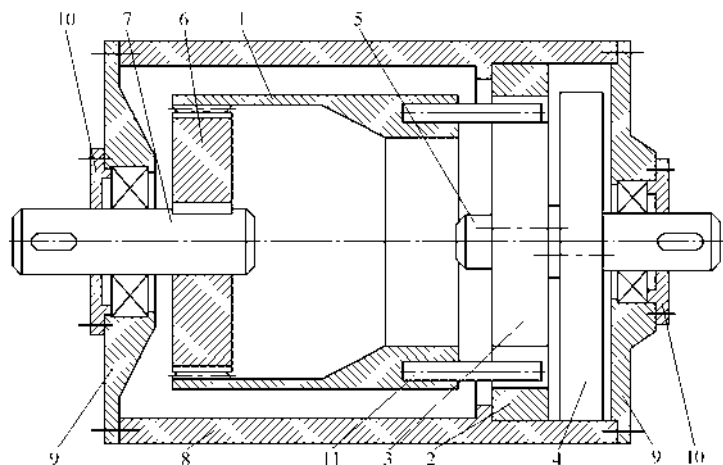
Конструктивная схема волновой роликовой передачи (ВРП): 1 – гибкое колесо; 2 – жесткое колесо; 3 – деформирующий диск; 4 – опорный диск; 5 – эксцентриковый вал; 6 – шлицевое колесо; 7 – выходной вал; 8 – корпус; 9, 10 – крышки; 11 – ролики
